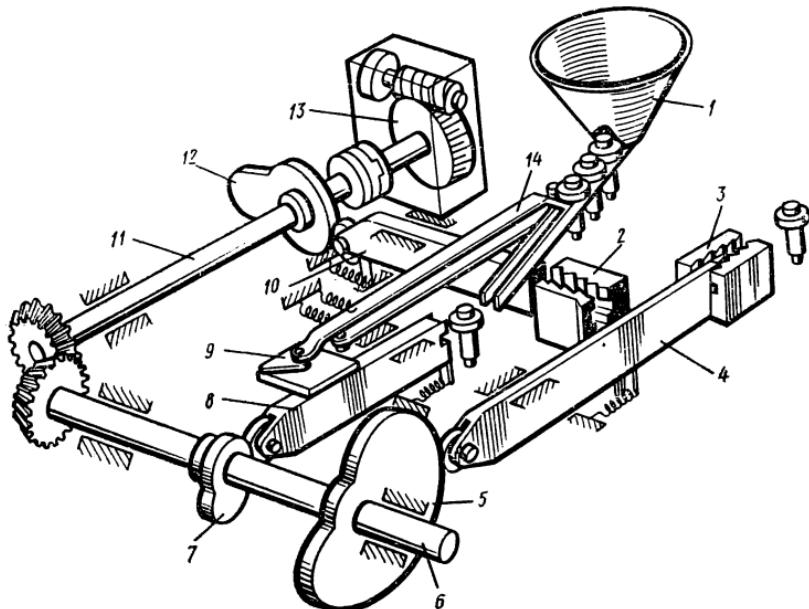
Принципиальная схема автомата для протягивания квадратов на цилиндрических заготовках:
